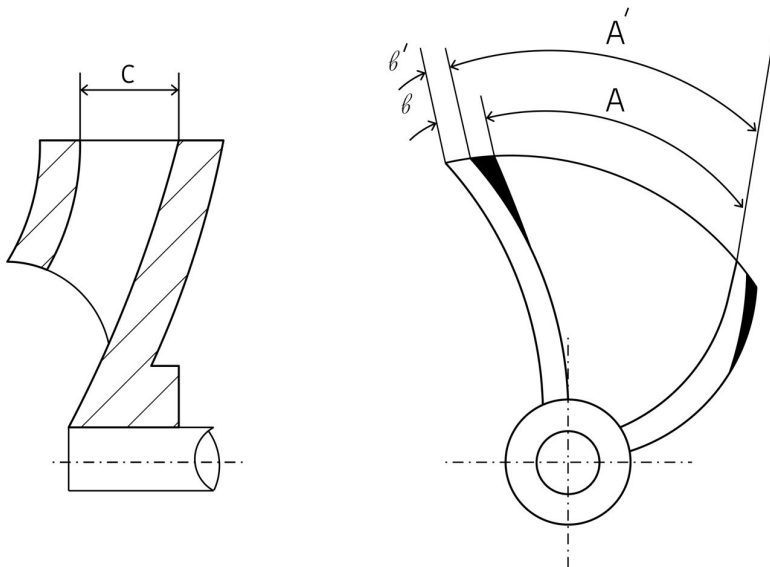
Схема підрізування робочого колеса по лопатках.
